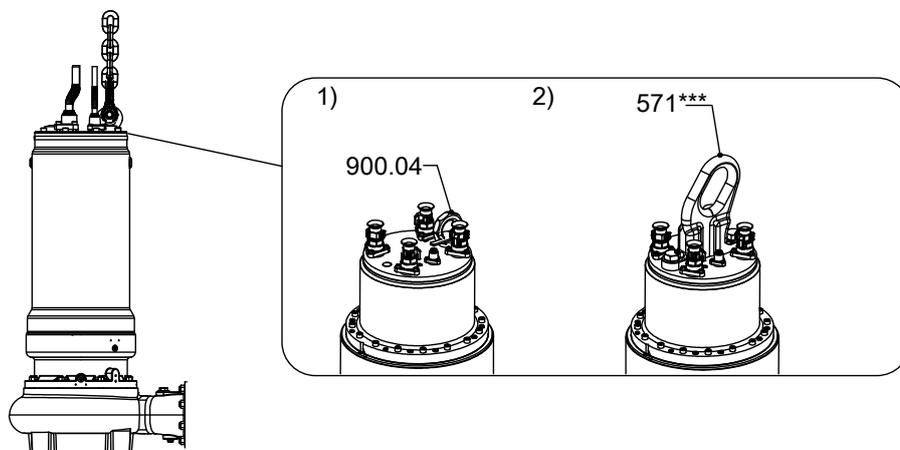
Colocación de la cadena/cuerda de izado - Instalación en zona seca
